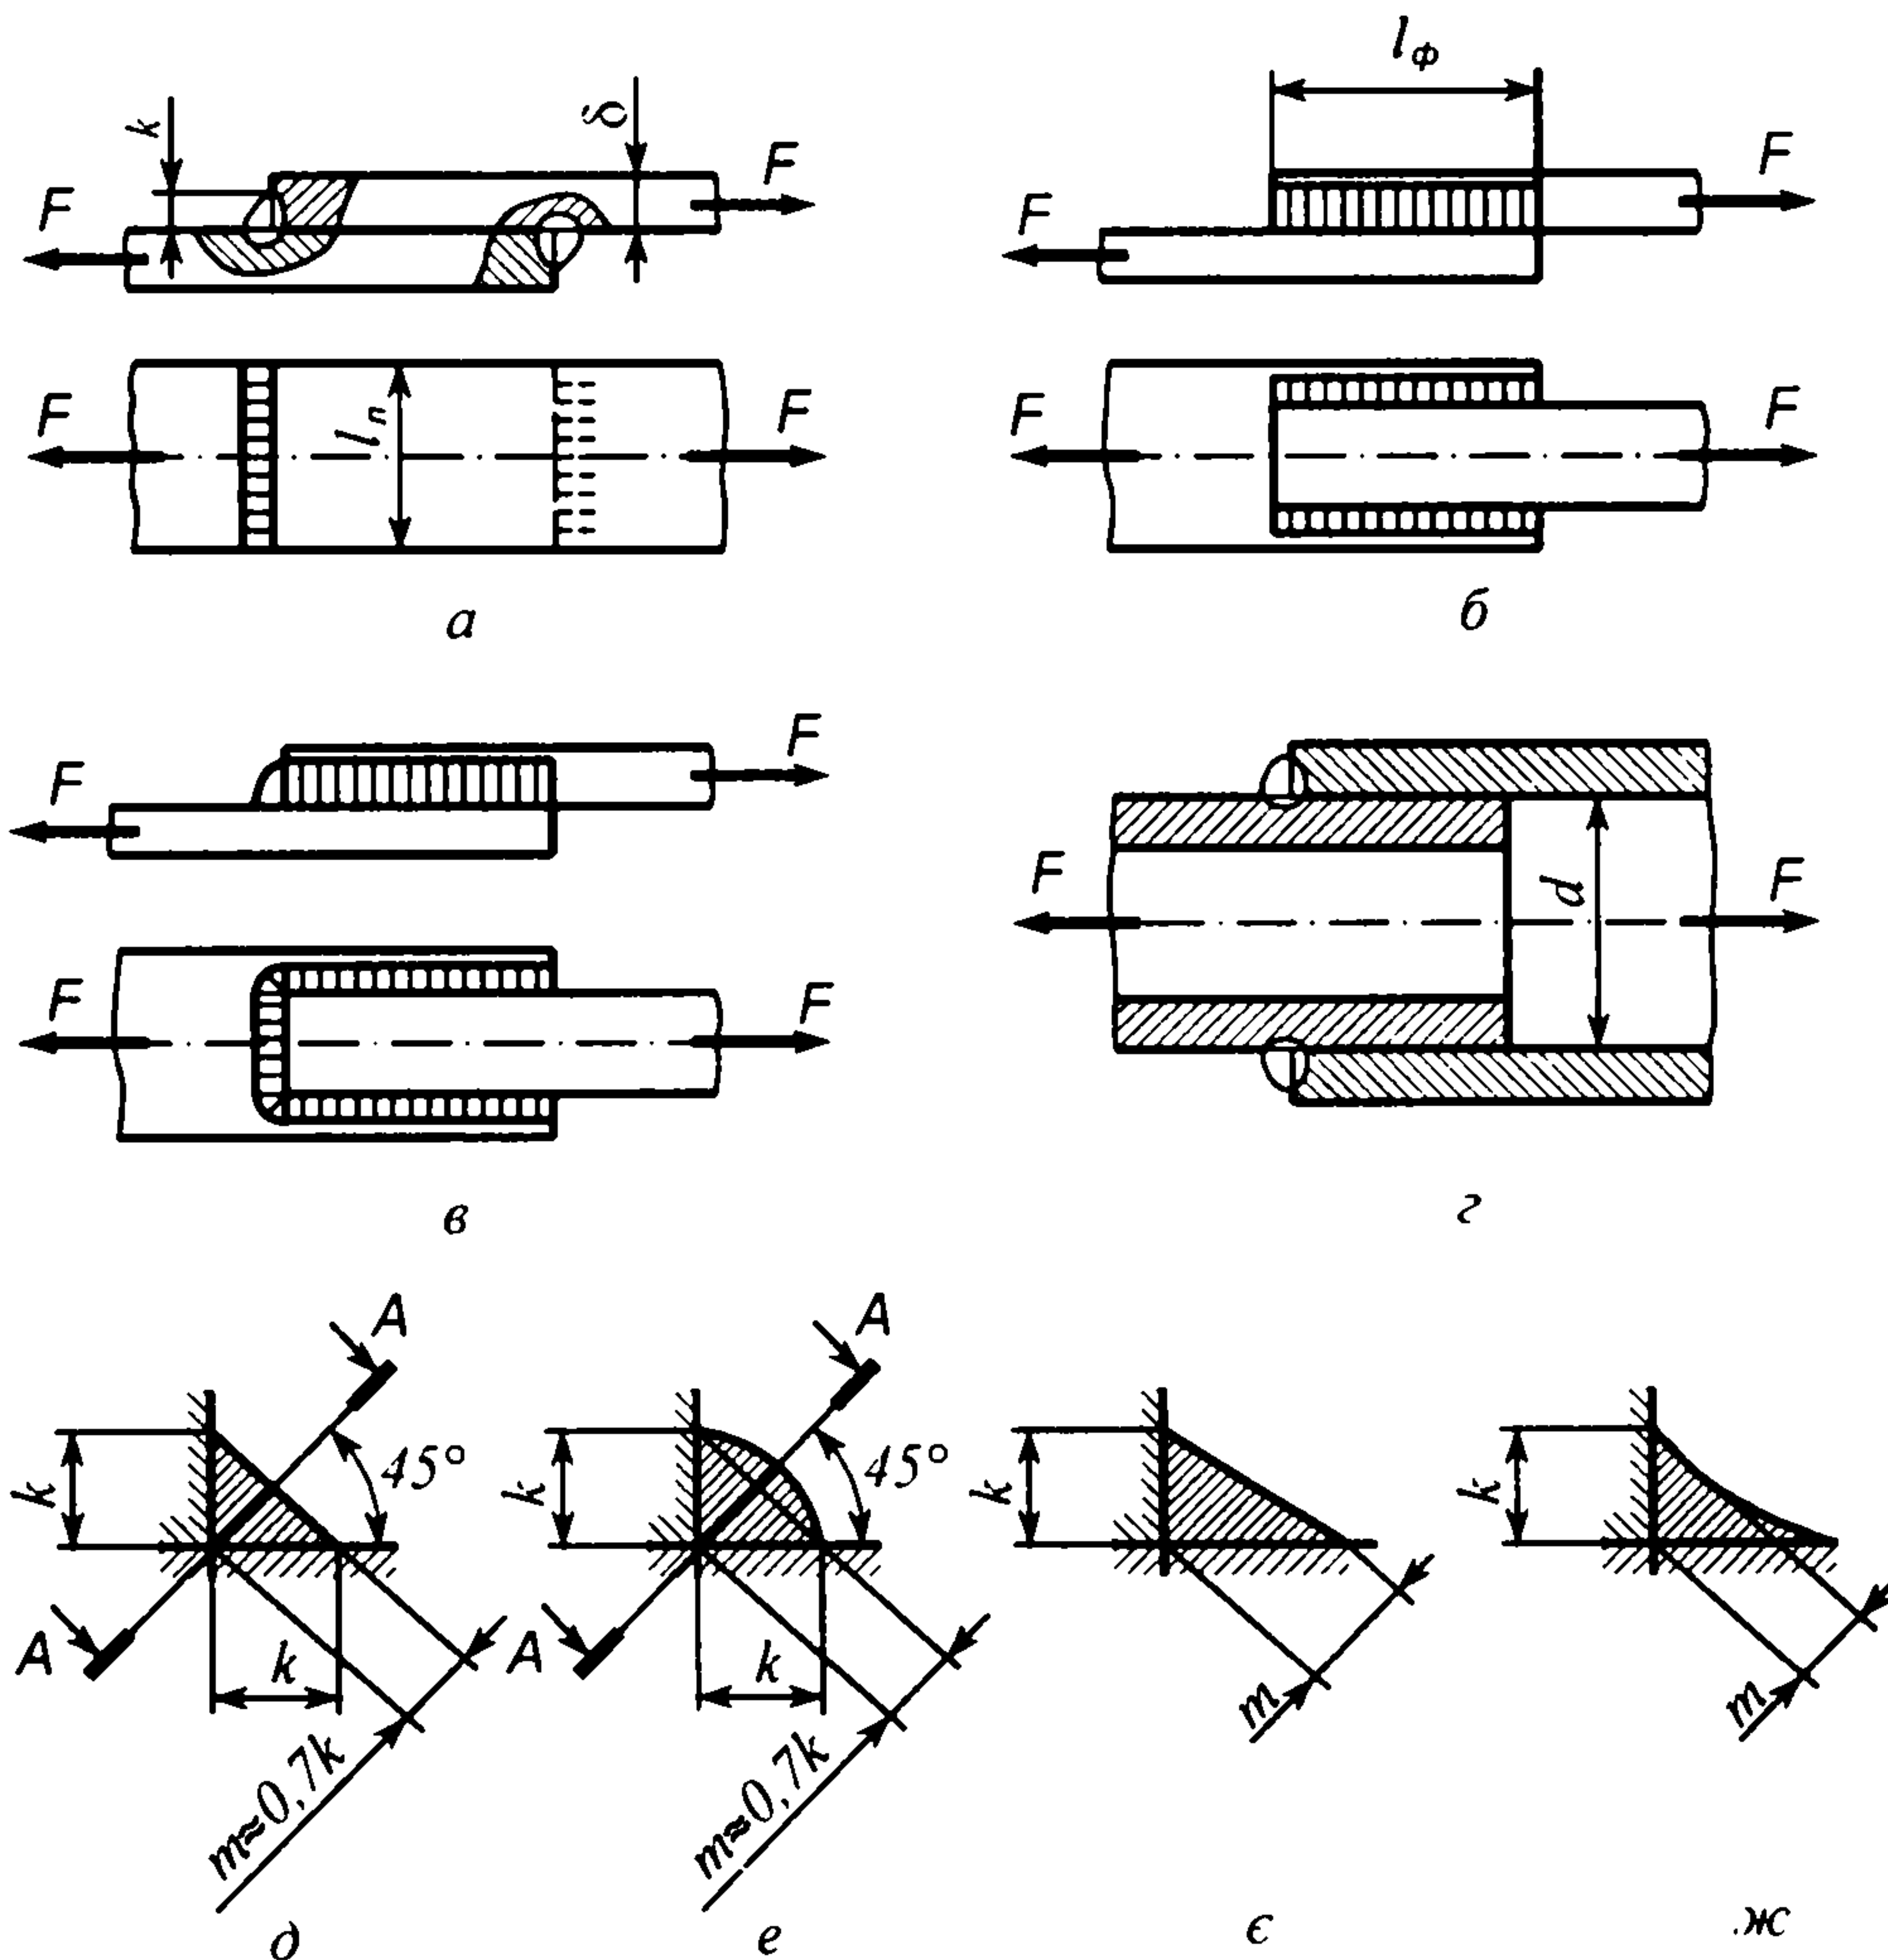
Зварні напусткові з'єднання та форми кутових швів
